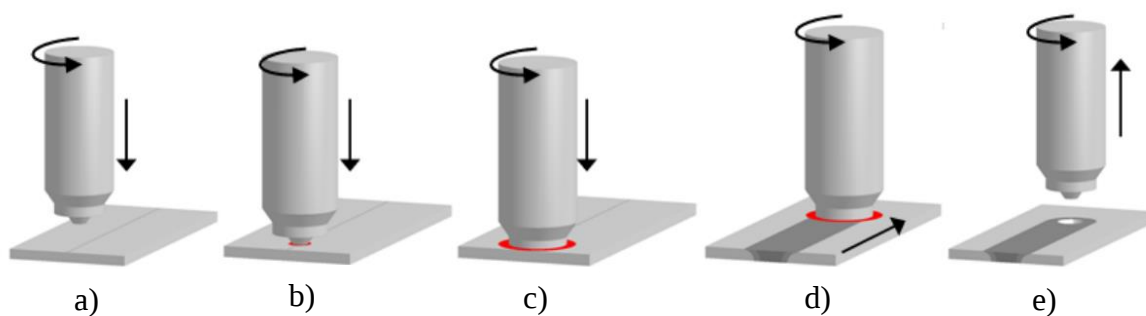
Etapas del proceso FSW: a) Posicionamiento de la herramienta; b) Penetración de la herramienta; c) Precalentamiento; d) Soldado; y e) Fin de la soldadura y retiro de la herramienta [14].
